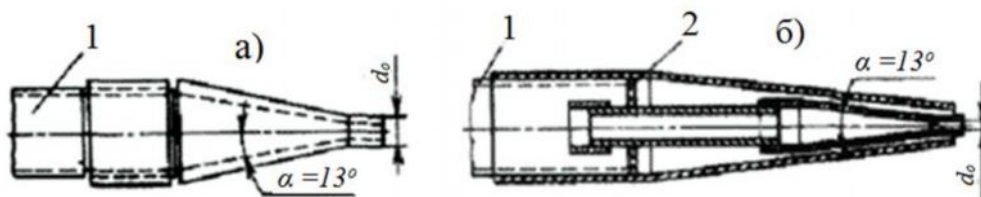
Насадки для гидропрокола: 1-труба; 2-диафрагма;
